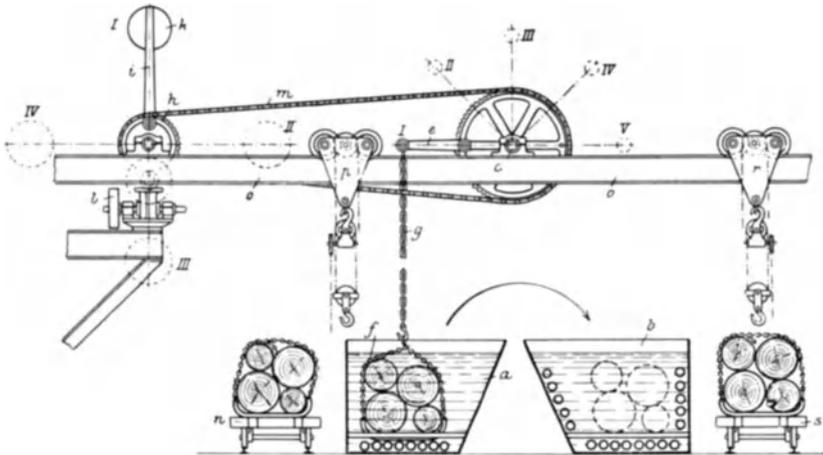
Hebezeug für Apparate zum Imprägnieren von Holz.
